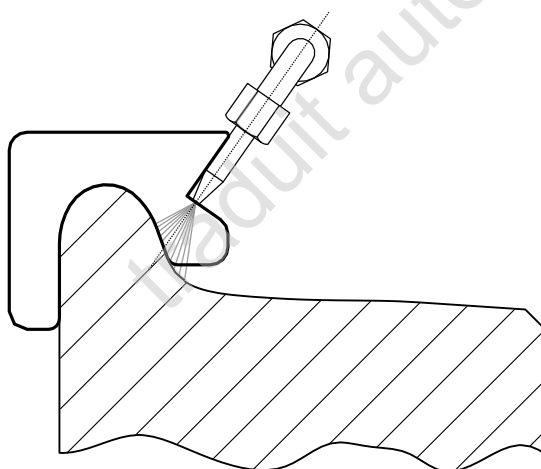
Jauge de réglage à partir du boudin de roue (exemple)
